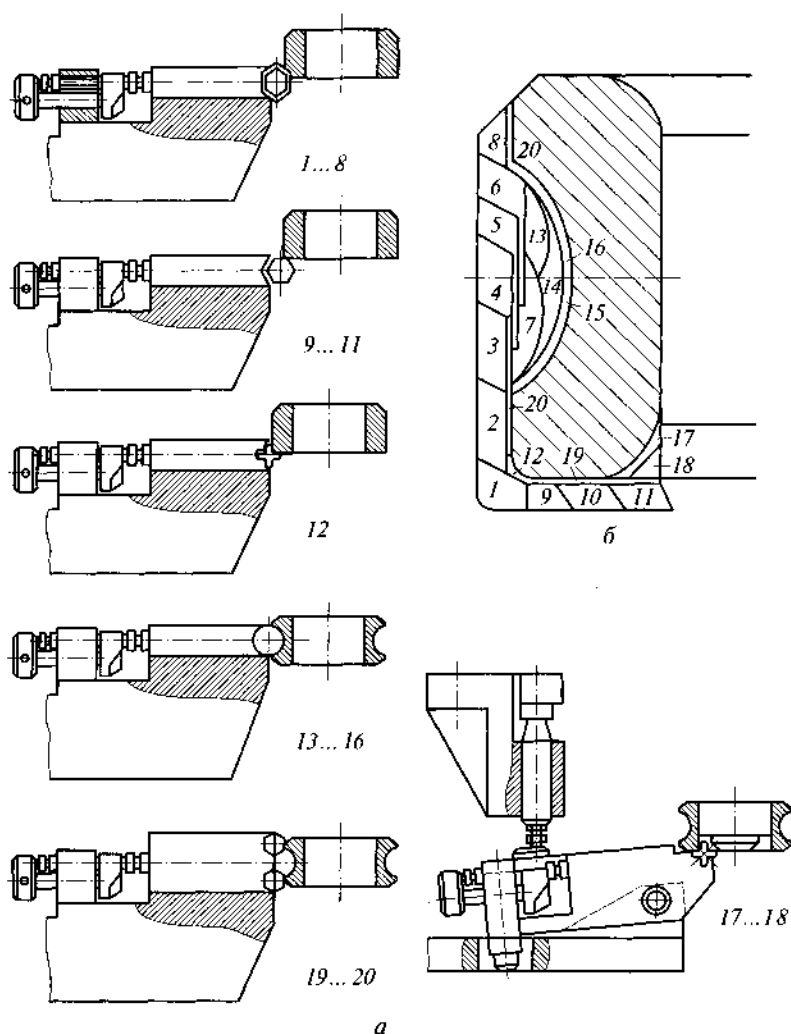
Обработка колец подшипников методом полутного точения:
